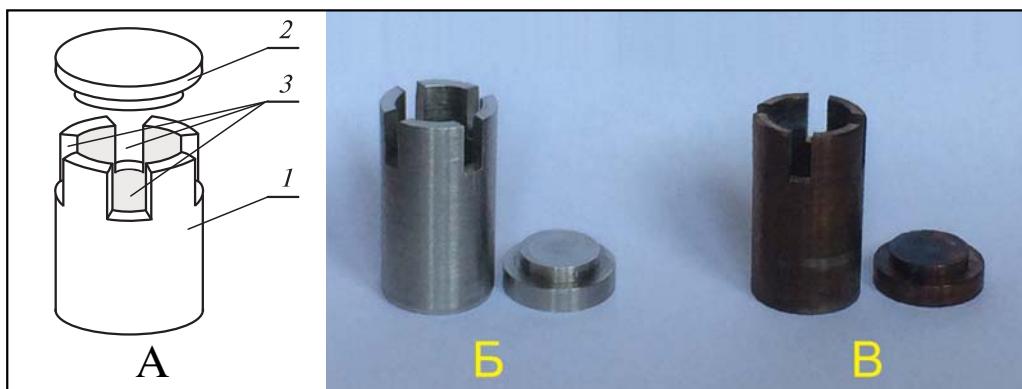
Дополнительный внутренний контейнер для обработки твердого образца водным флюидом:
